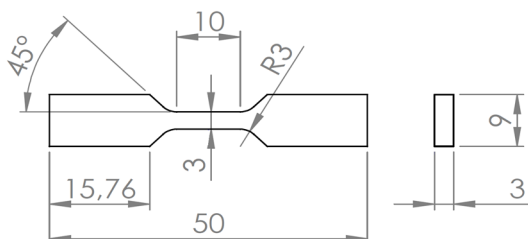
Geometria com dimensões em mm do corpo de prova #1.
